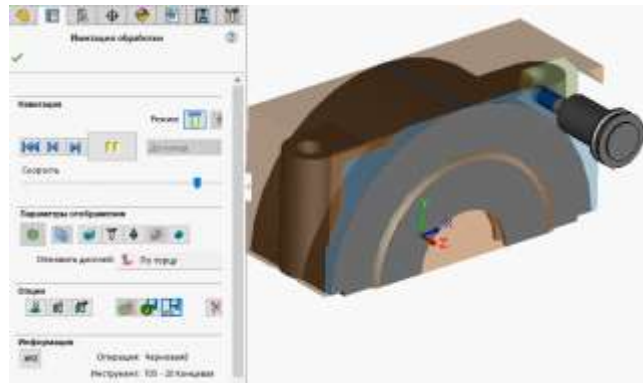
Симуляція обробки заготовки на металорізальному верстаті у САМ-модулі SolidWorks.
